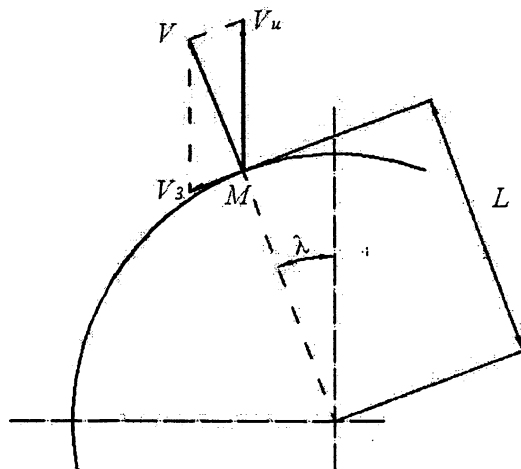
Схема скоростей при обработке торцовых зубчатых контуров
